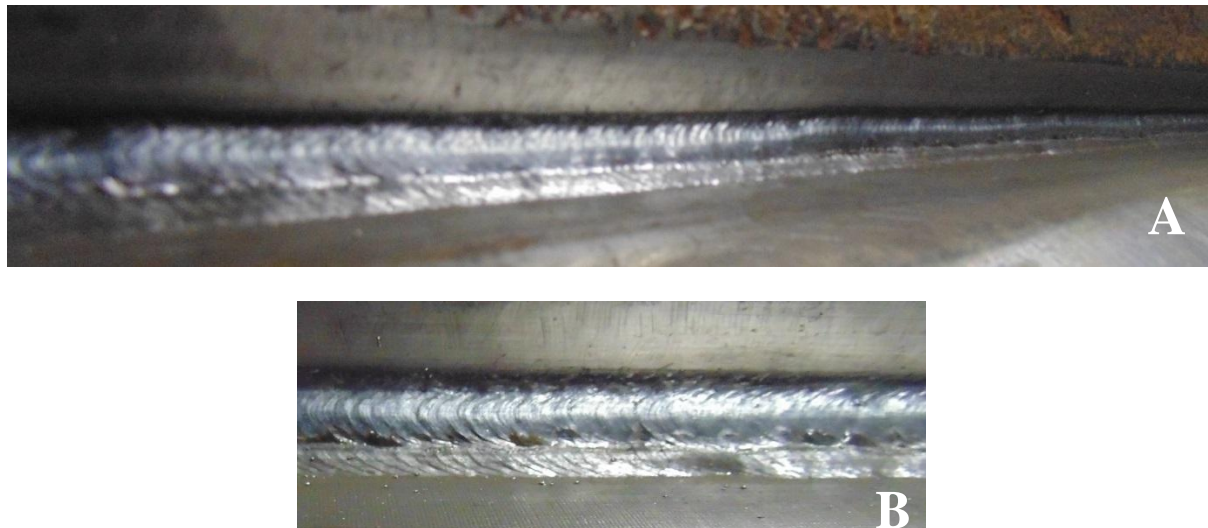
Aspecto superficial dos cordões soldados na posição horizontal
